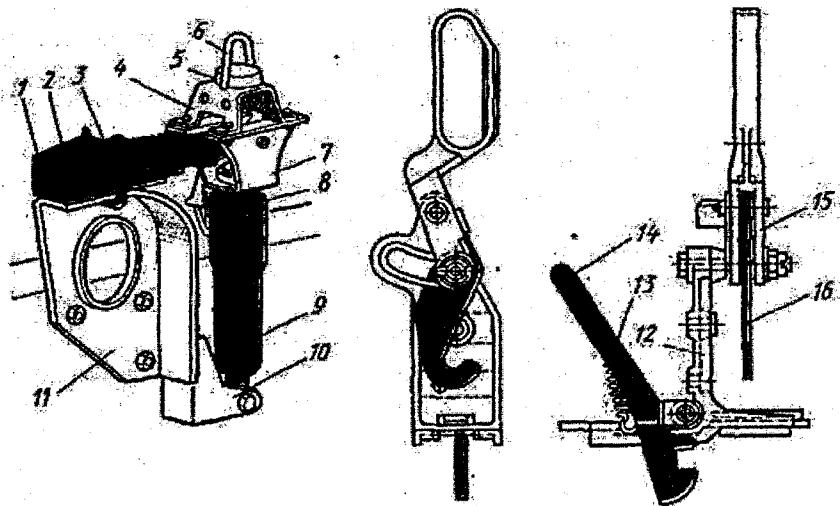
Задня опора і запірний пристрій кабіни вантажного автомобіля КамАЗ-5320
